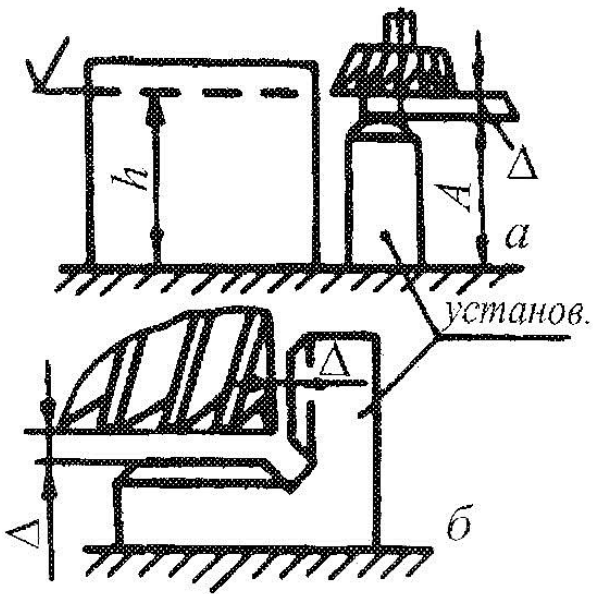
Висотний (а) і кутовий (б) установи для фрезерних пристроїв
